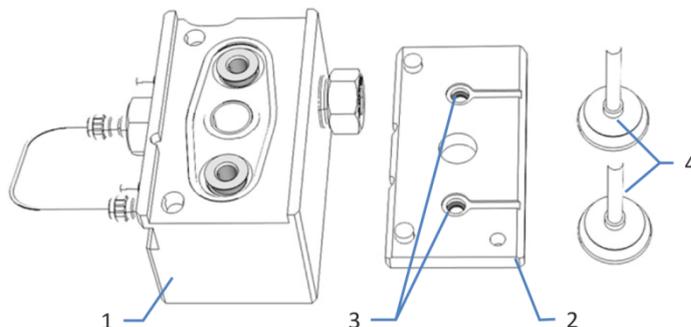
Tête de pompe, plaque de rinçage des joints et pistons retirés
